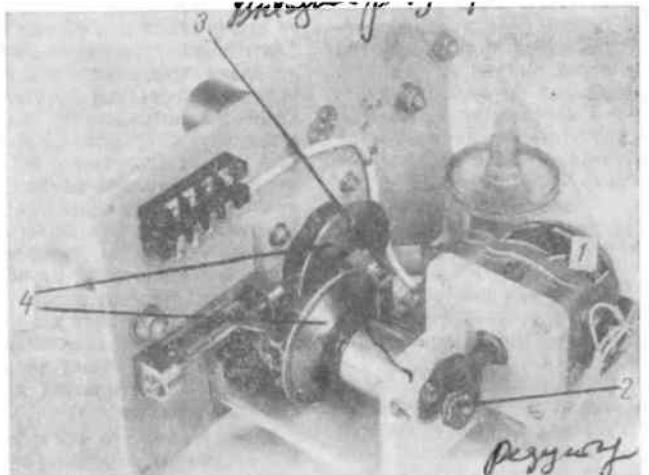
Узел лакировки (вид сзади) Режущий механизм Режущий
